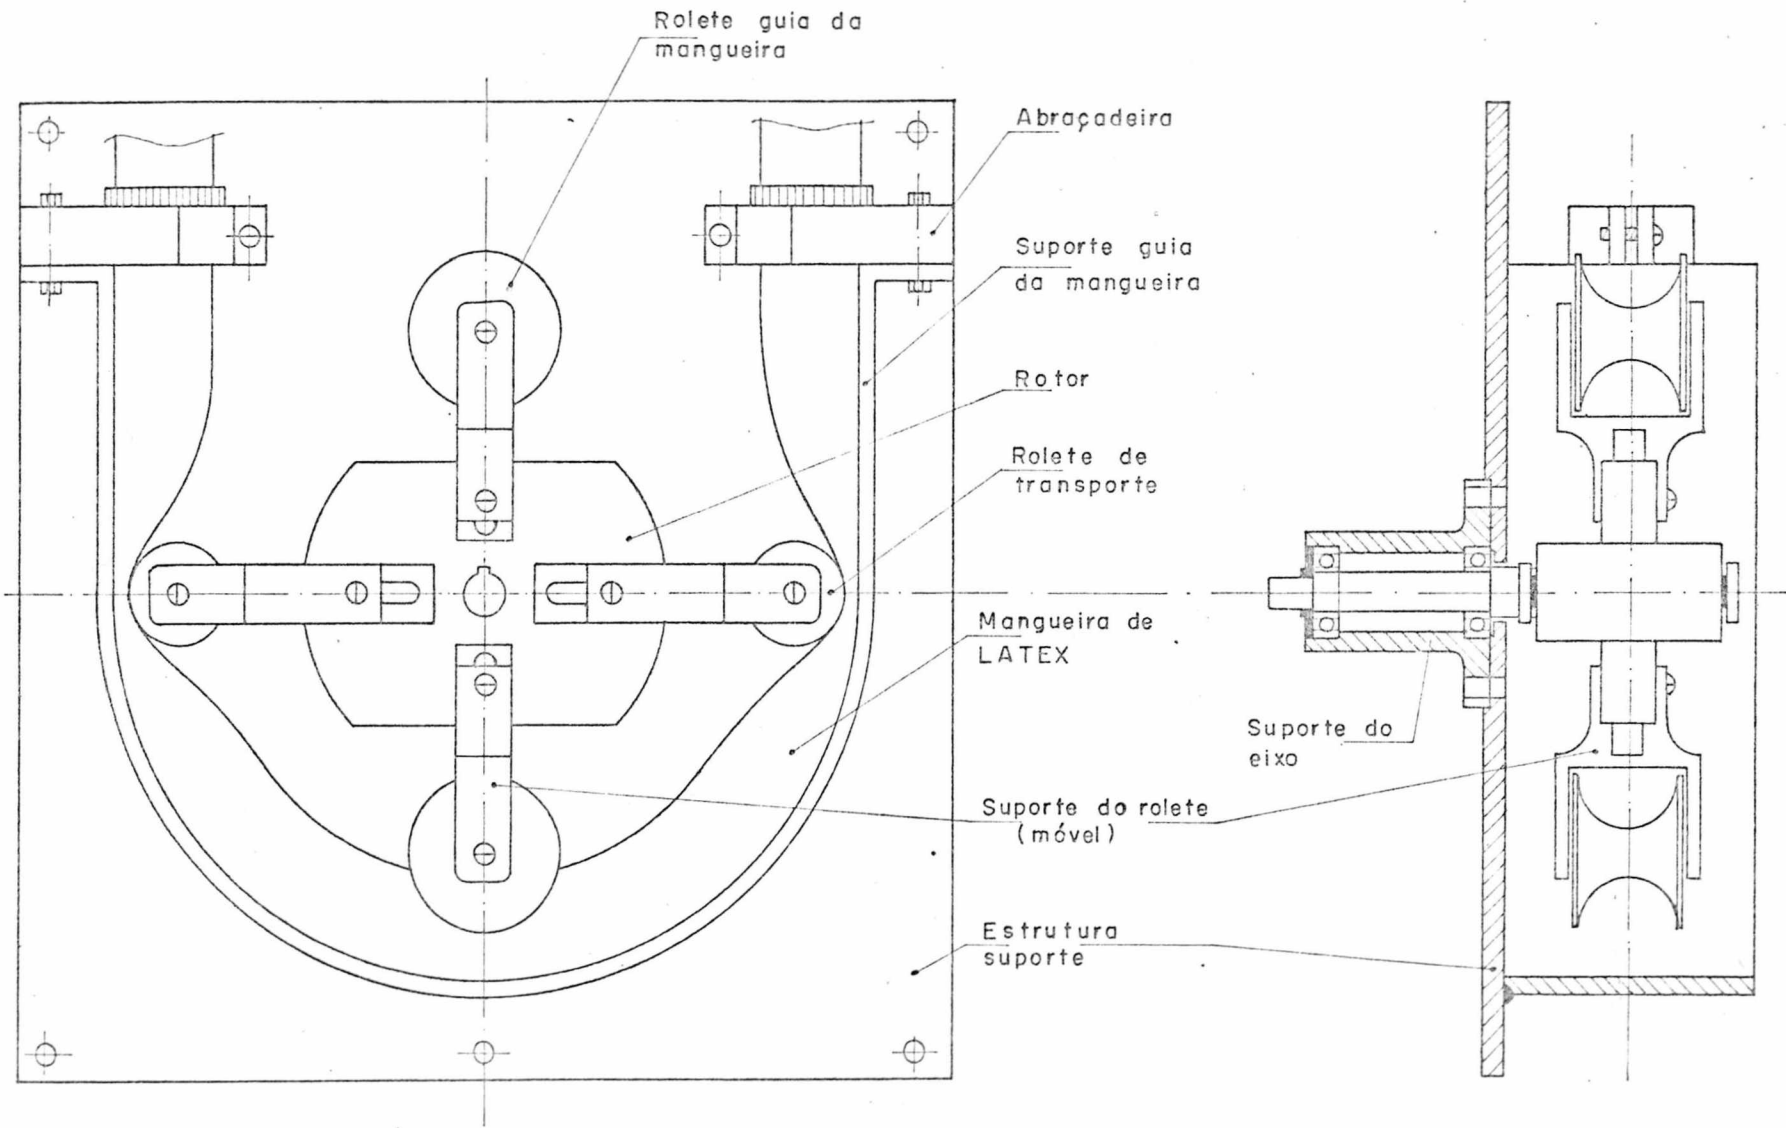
= Montagem do rotor da bomba sobre seu suporte
